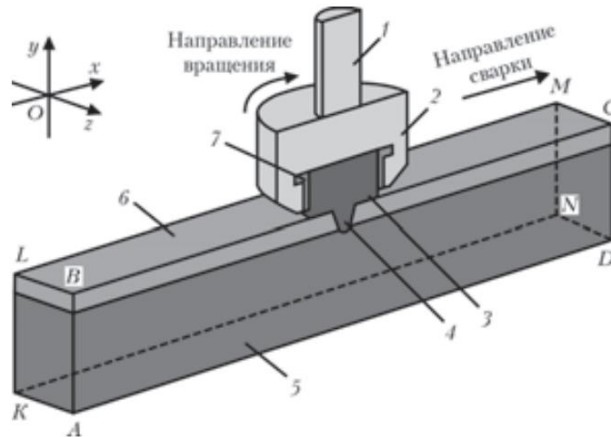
Розрахункова область (повздовжнє січення площиною ABCD): 1-стальний вал приводу; 2 – стальна державка; 3, 4 – буртик і штир робочого елемента; 5, 6 – зварні деталі; 7 – твердосплавна обойма [7].
